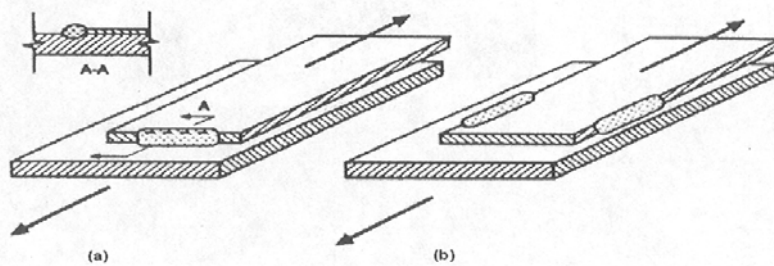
Modos de falla de soldaduras de filete. (a) Soldaduras transversales; (b) Soldaduras longitudinales.
